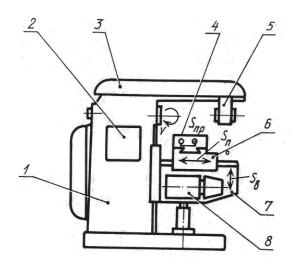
Горизонтально-фрезерный станок: 1 — станина; 2 —коробка скоростей; 3 — хобот; 4 — стол; 5 — подвеска; 6 — салазки; 7 — консоль; 8 — коробка подач.
